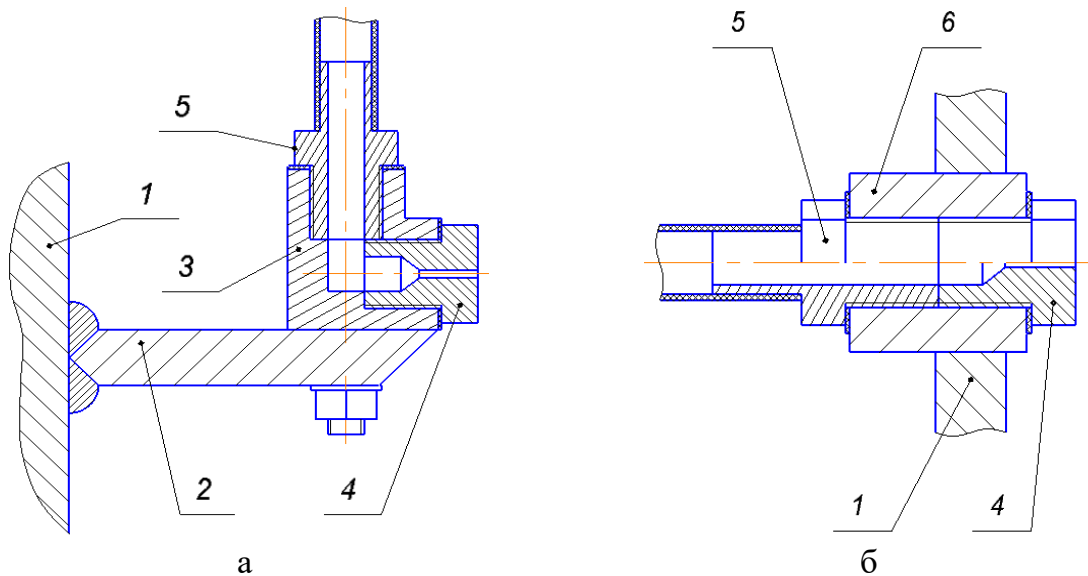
Схема имитатора типа «протечка продукта через стенку» прижимного (а) и приварного (б) исполнения
